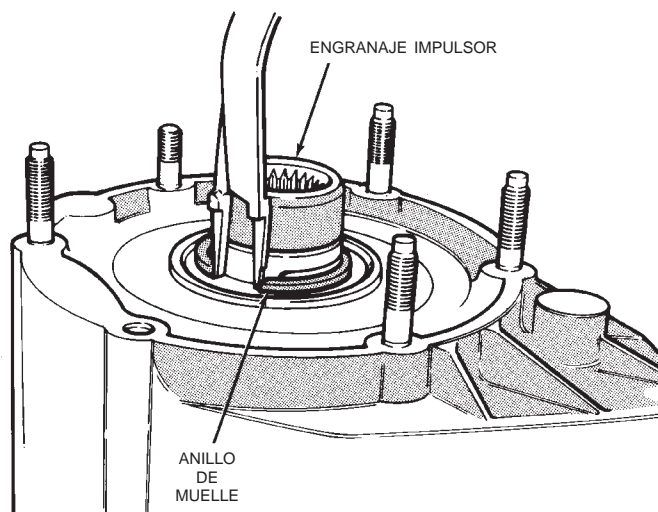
Instalación de anillo de muelle de engranaje de baja
